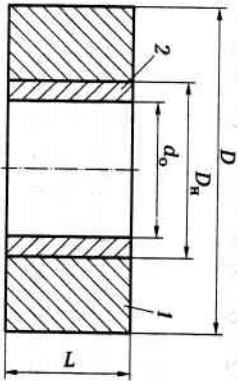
Сборочный чертёж прессового соединения деталей к заданию 7.31
